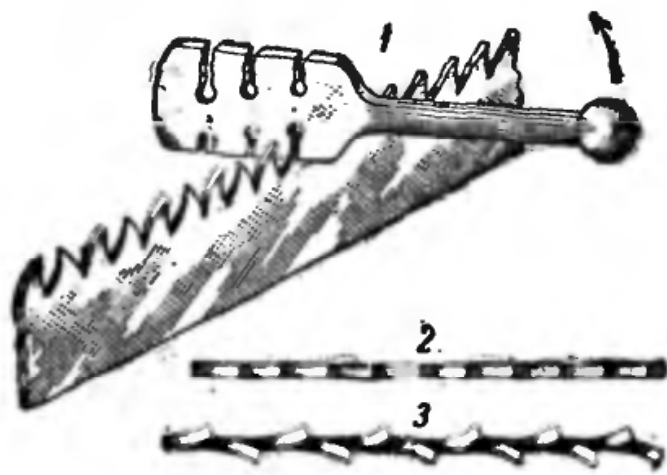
Разводка для пил 1—стальная пластинка с прорезами; ширина прорези должна соответствовать толщине полотна пилы; 2—полотно пилы с неразведёнными зубьями; 3—с разведёнными зубьями.
